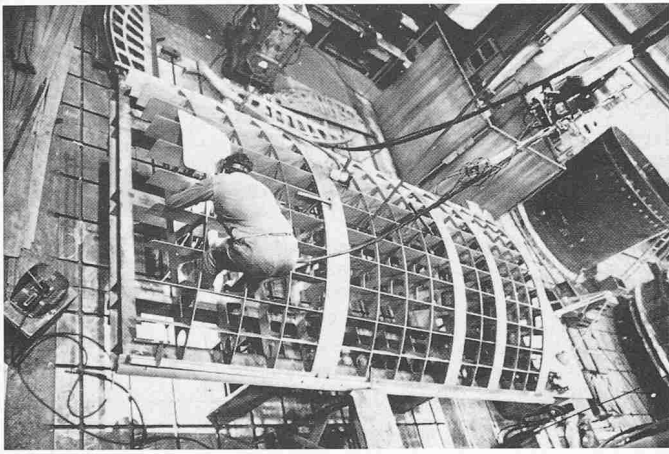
Montage der Blechrahmen auf dem Grundgerüst
